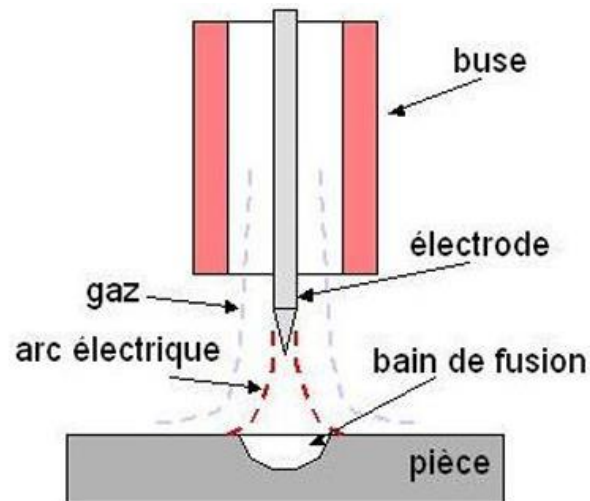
Soudage à l'arc électrique.[22]
